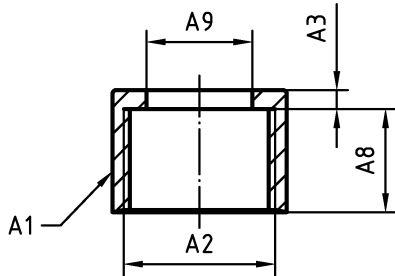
Gewindeanschluss 3/8 ISO 228-1
